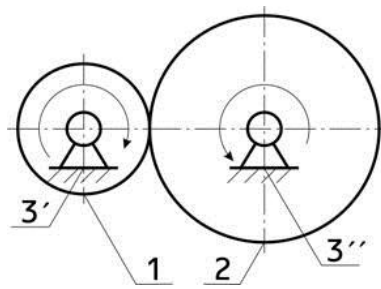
Зубчатый механизм с внешним зацеплением
